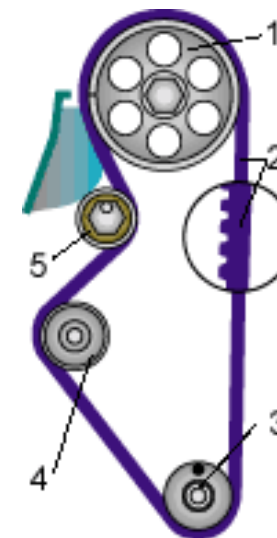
Схема привода распределительного вала на примере двигателя автомобиля ВАЗ 2108:
